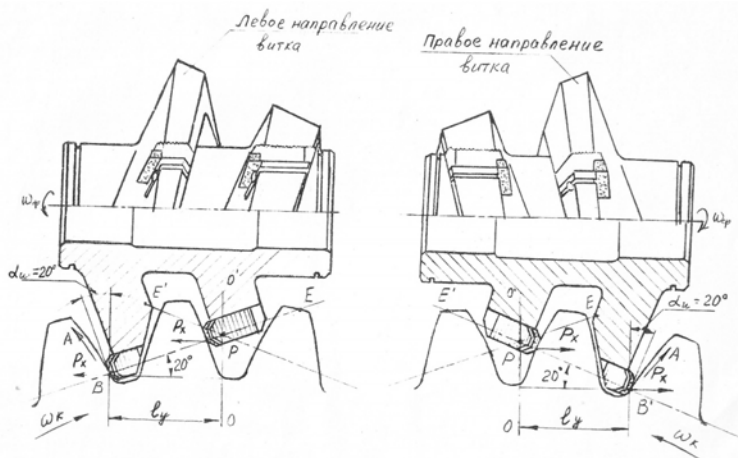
Схема обработки колеса корпусами фрезы с различным направлением витков
